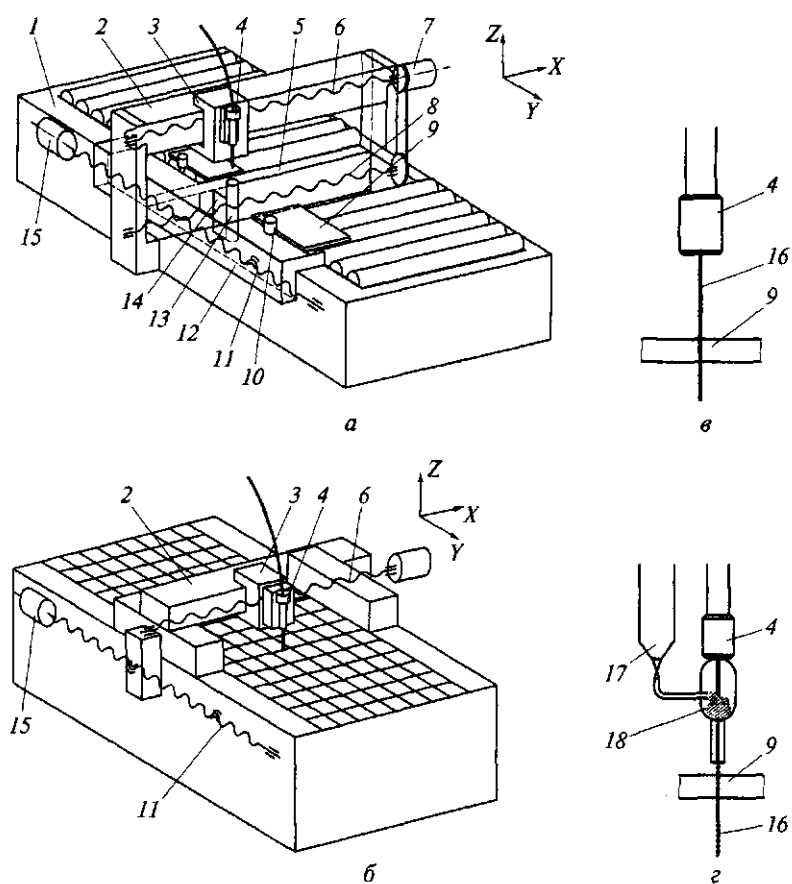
Типовые компоновки водоструйных установок с неподвижным (а) и подвижным (б) порталом и принципиальные схемы режущих головок для гидрорезки (в) и гидроабразивной резки (г):
